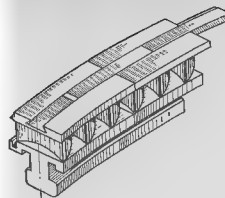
Фото сварного пакета рабочих лопаток регулирующей ступени мощной турбины
